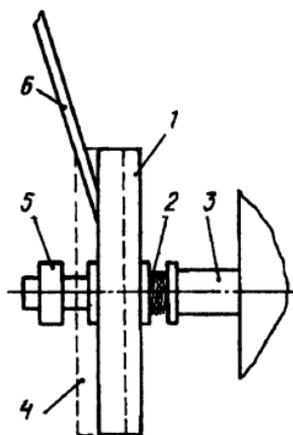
Схема крепления наждачного круга на валу точила: 1 — наждачный круг; 2 — пружина упора; 3 — вал; 4 — положение наждачного круга при отсутствии контакта с ножом; 5 — упругий упор; 6 — нож
